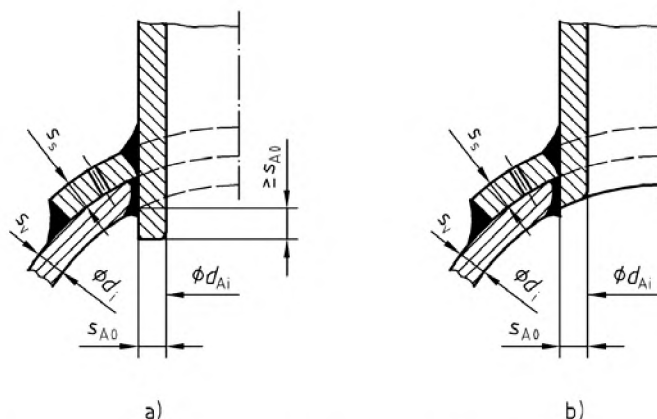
Отверстие с упрочняющим слоем и патрубком с полным проплавлением (сварные швы, применяемые для цилиндрических обечайки с доступом внутрь)
